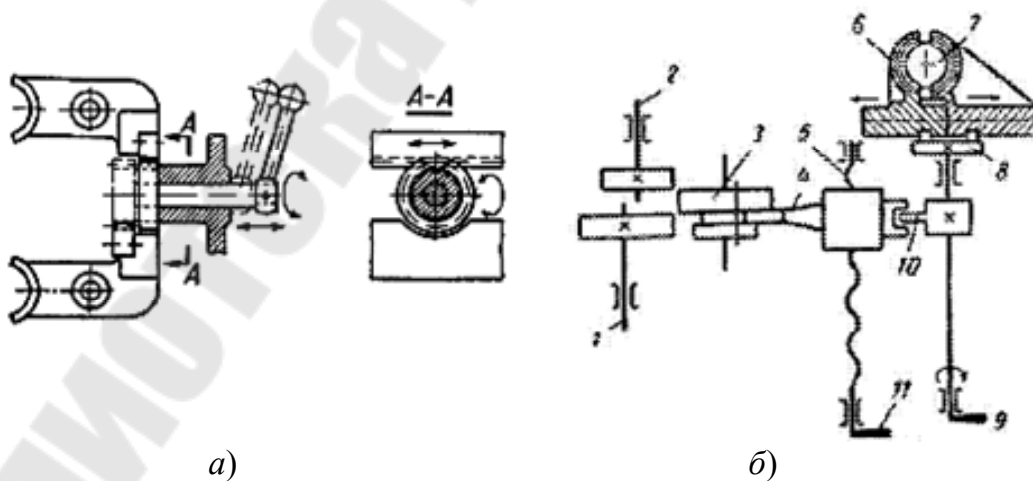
Блокировка деталей управления, движущихся параллельно (а) и одновременного включения ходового валика и ходового винта токарно-винторезного станка (б)
